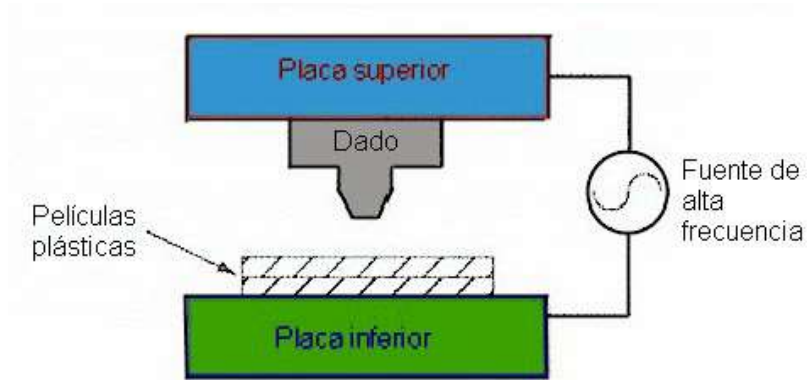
Esquema de soldadura por alta frecuencia (Tecnología de los Plásticos, 2013)
